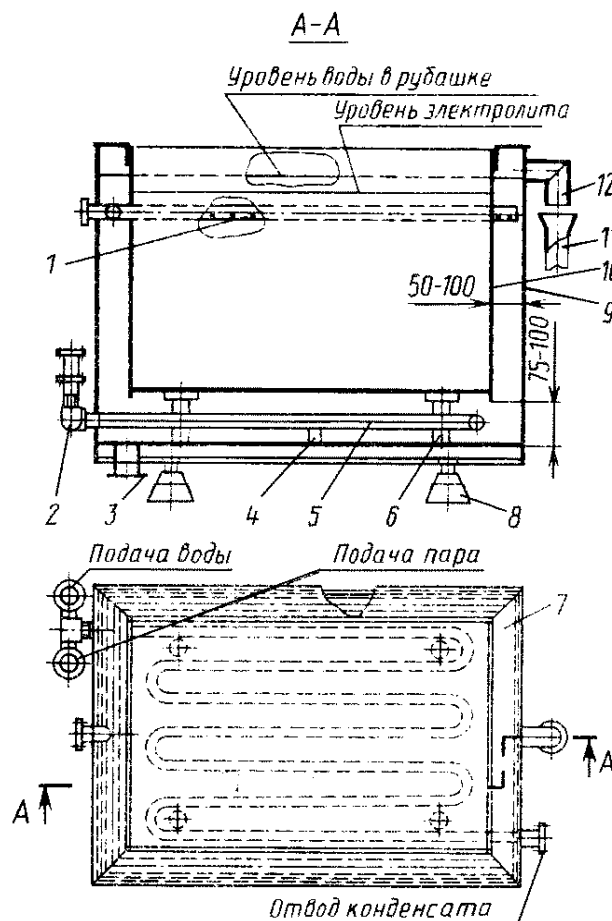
Ванна с водяной рубашкой: 1 – труба подачи воды в рубашку; 2 – тройник; 3 – патрубок слива воды из рубашки; 4 – опора; 5 – змеевик; 6 – ножка рабочей ванны; 7 – верхняя обвязка из уголков; 8 – изолирующая ножка; 9 – внешняя ванна; 10 – рабочая ванна; 11 – воронка; 12 – сливной патрубок.
